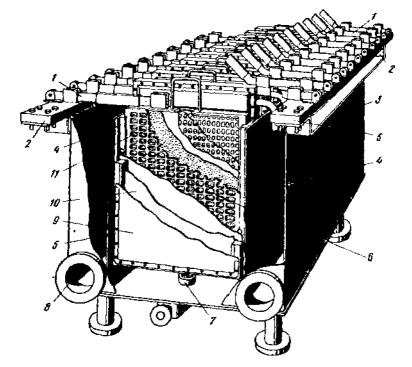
Электропизер ЗУ-1М: I — корпус; 4 — направляющие; 5 — планки; 6 — катор; 7 — штуцер; 8 — патрубки для вывода католита и аполита; 9 — мембрана; 10 — янор; 11 —винипластовая сетка
